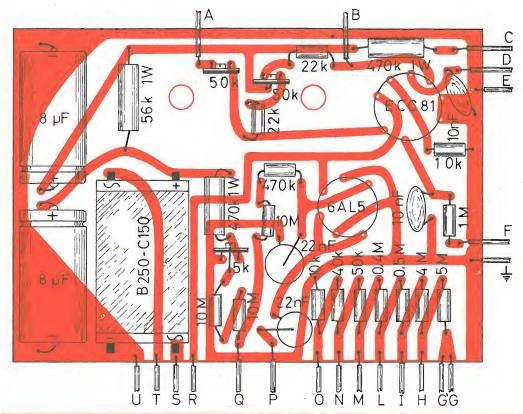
Circuito stampato visto dal lato dei componenti.
